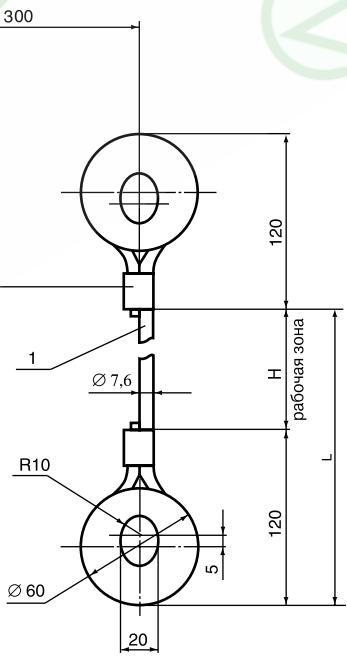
Общий вид, габаритные и установочные размеры передающего преобразователя
